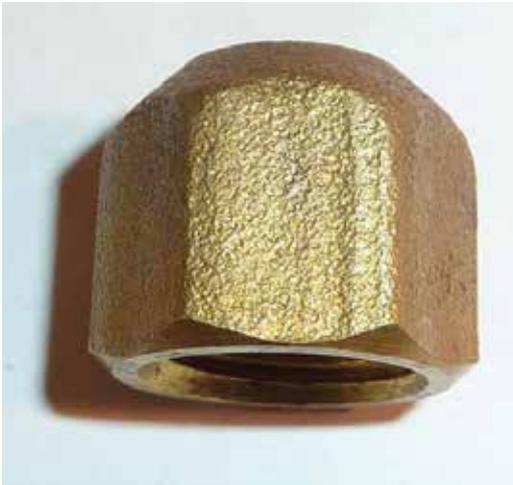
Tampa sextavada com superfície de vedação de bronze cônica.
